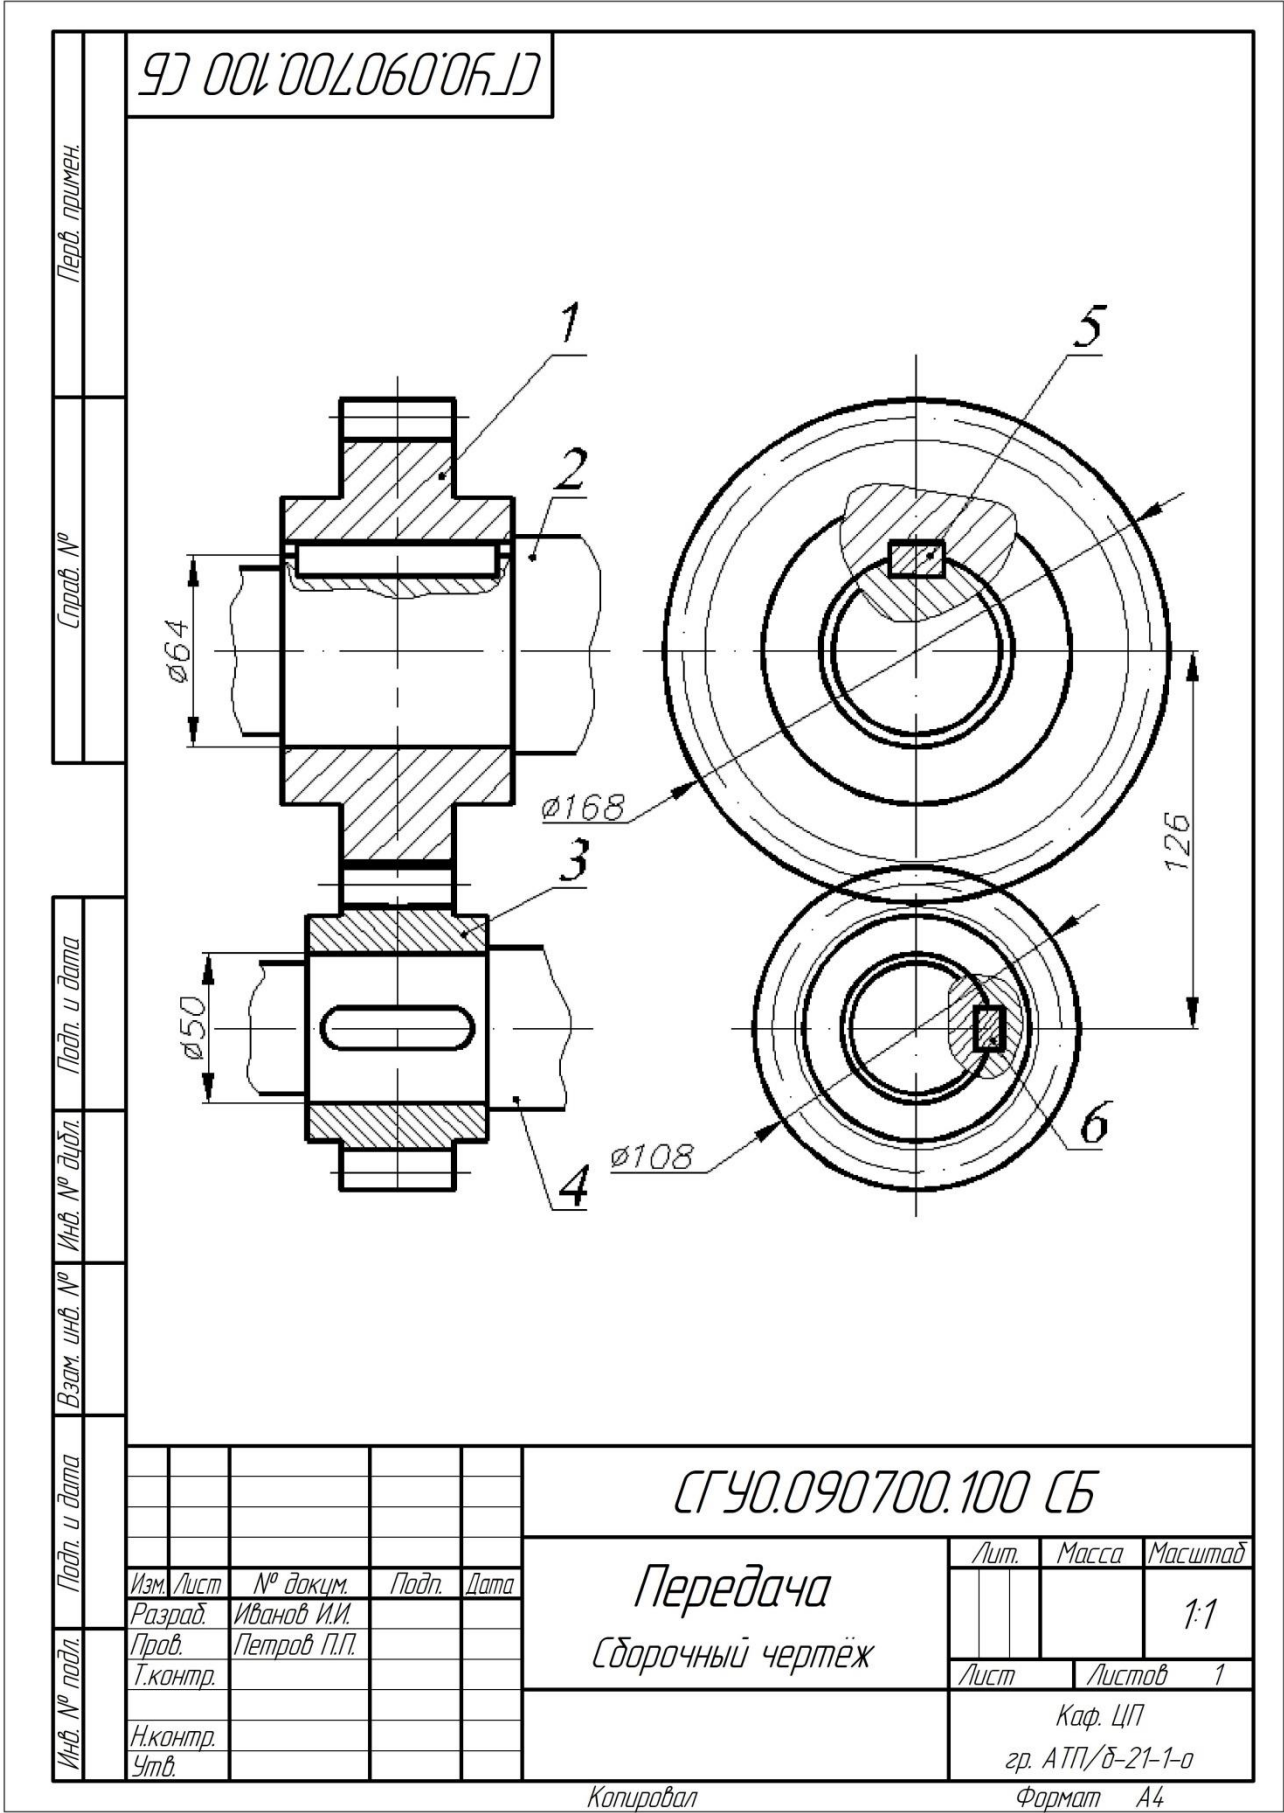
Сборочный чертеж цилиндрической зубчатой передачи
